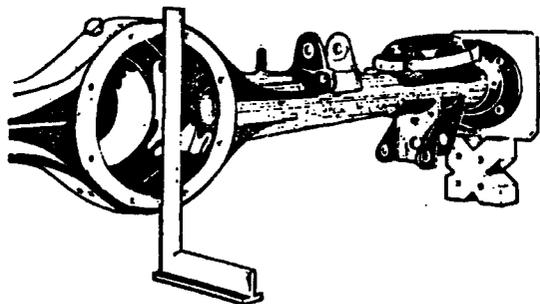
Проверка перпендикулярности поверхности крепления редуктора
